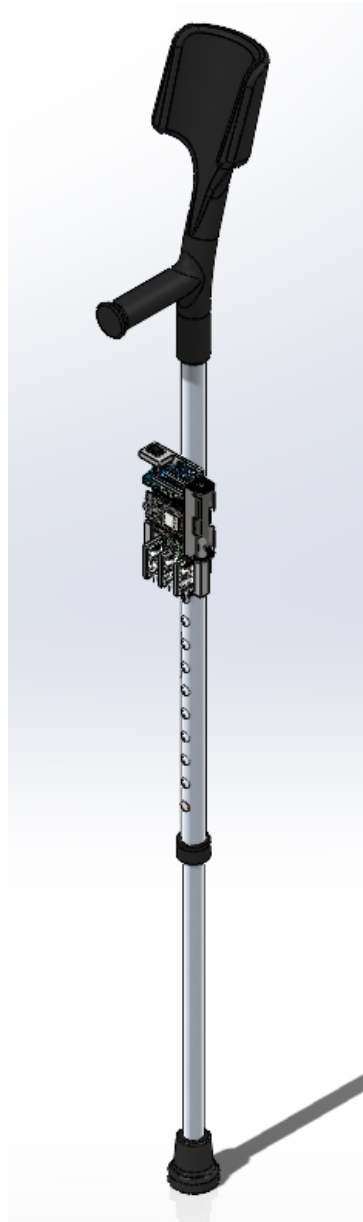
CAD protótipo de fixação da eletrônica embarcada
